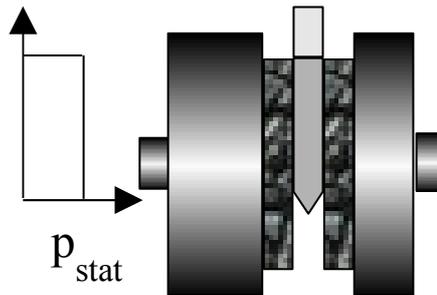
Gleichmässiger Bearbeitungsdruck über die ganze Werkzeuglänge
